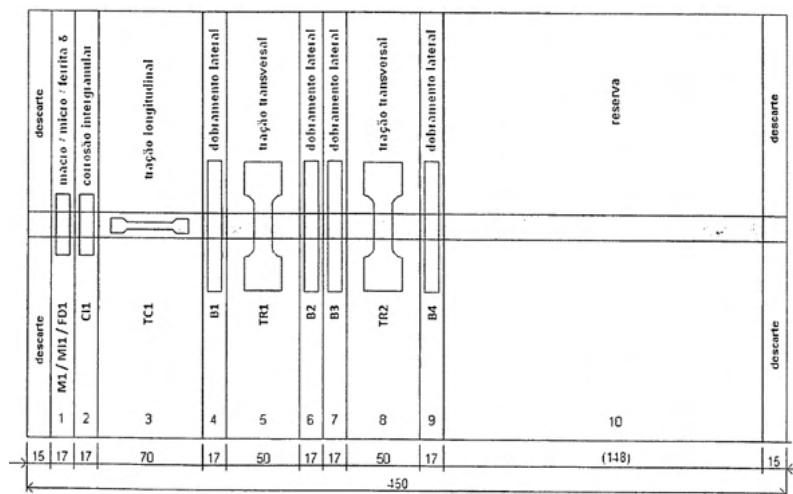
Layout da retirada dos Corpos de Prova (CP's) das amostra (unidades em mm)
